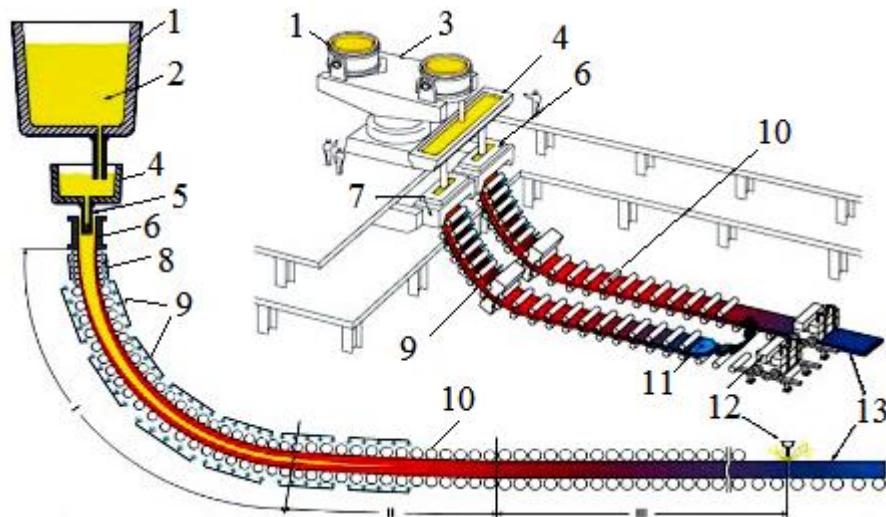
Схема технологічної лінії криволінійної МБЛ, де 1 – розливний ківш; 2 – рідка сталь; 3 – поворотний стелд; 4 – проміжний ківш; 5 – погрузна склянка; 6 – водоохолоджений кристалізатор; 7 – механізм гойдання кристалізатора; 8 – підтримуюча система; 9 – форсунки зони вторинного охолодження; 10 – ролики; 11 – запал; 12 – газорезка; 13 – готовий сляб
